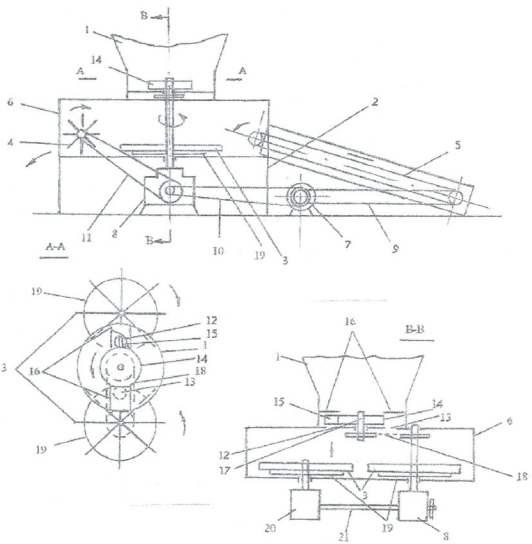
Установка для внесения сухого консерванта в силосную массу. 1-бункер – дозатор; 2-рама; 3-разбрасыватели; 4-битер; 5-погрузчик; 6-кузов; 7-электродвигатель; 8, 20-редукторы; 9,10,11-механизмы передач; 12,13 – окна; 14-ротор; 15-лопасть; 16-kozyрки; 17,21-валы; 18-цепная передача; 19-диски
